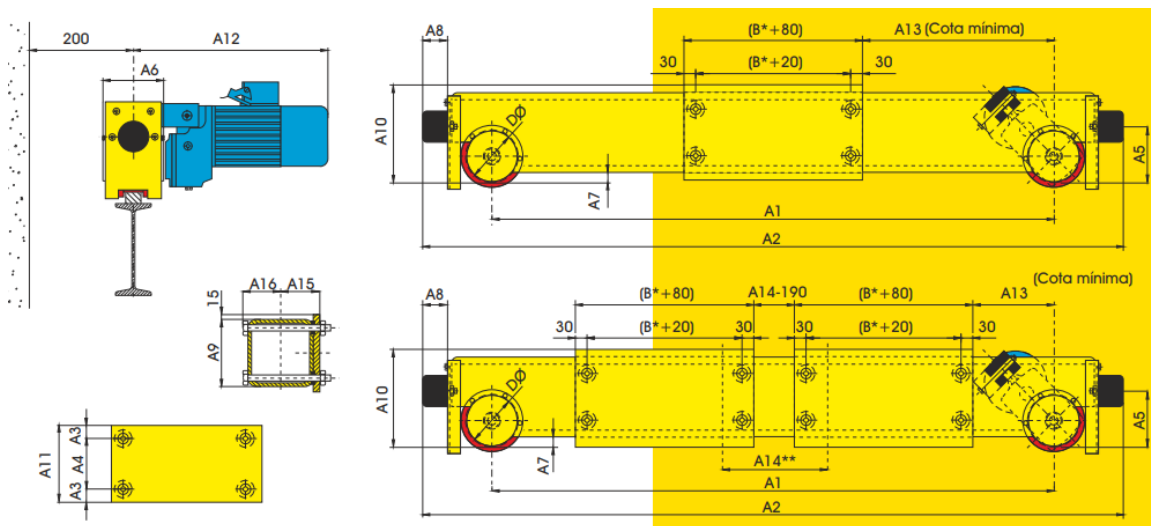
Dimensiones cajón testero para viga monorraíl
